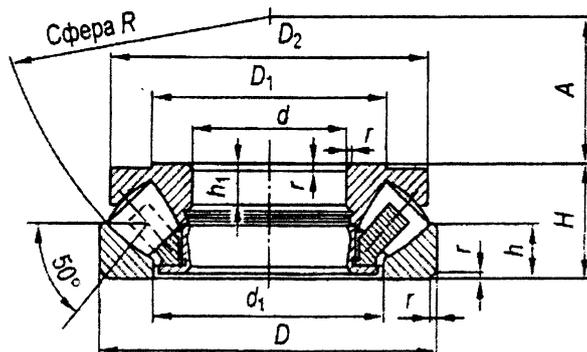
Подшипник роликовый упорно-радиальный сферический исполнения 39000
